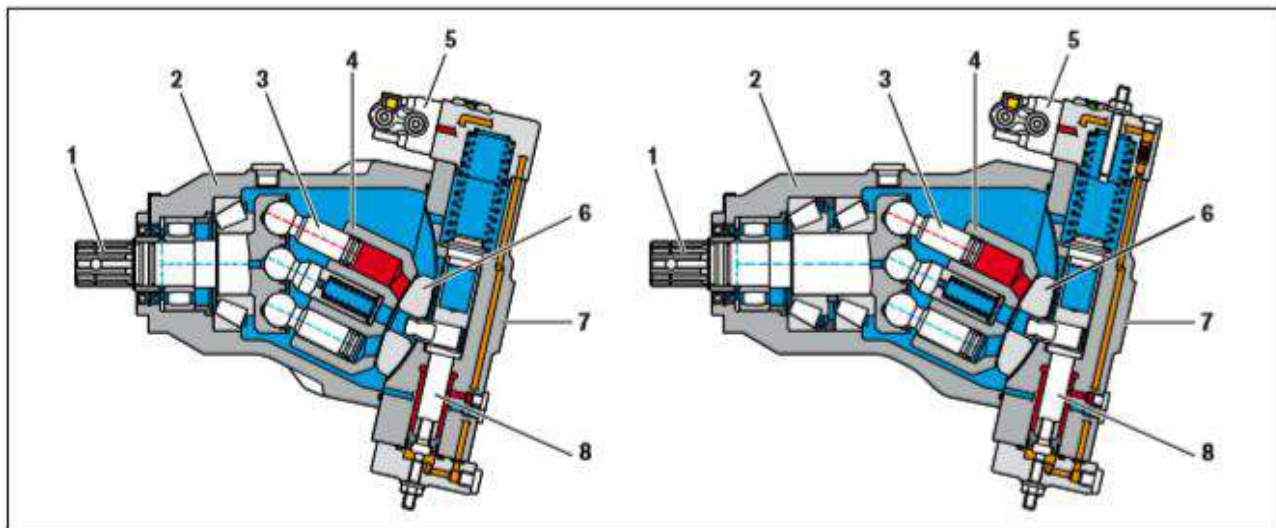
Гидронасос Rexroth серии A18VO: 1 – приводной вал, 2 – корпус, 3 – конический поршень, 4 – блок цилиндров, 5 – регулирующий клапан, 6 – распределительный диск, 7 – задняя крышка, 8 – золотник регулятора
